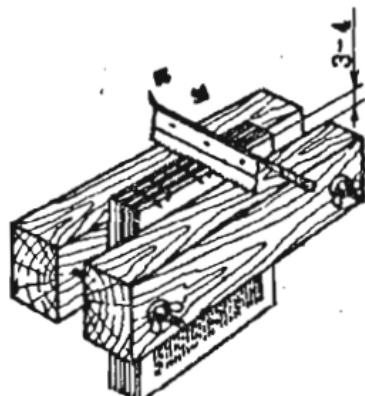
Пропиливание пазов в корешке книжного блока с бесшвейным креплением листов
